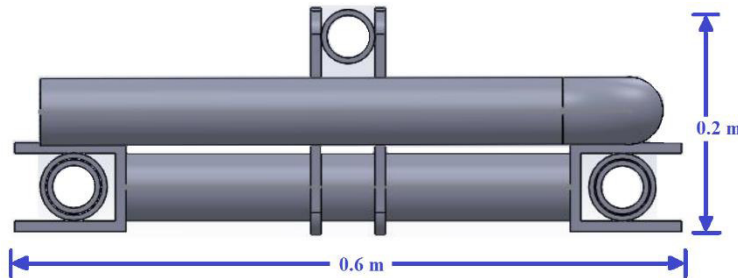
Grúa en posición acostada, base retraída y soporte superior desmontado, primer ensamble, vista frontal
